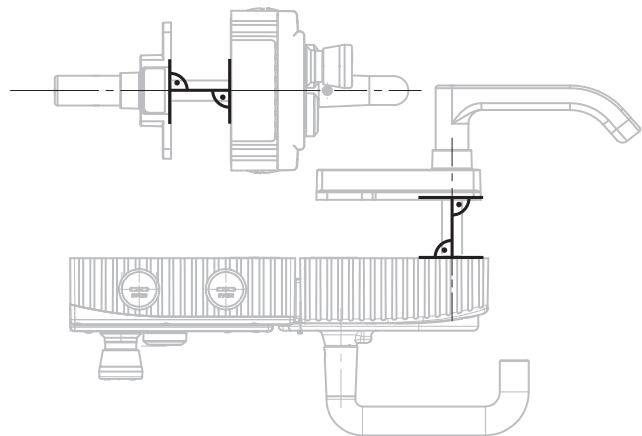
Monteringsexempel för högersvängd dörr (översiktsbild)
